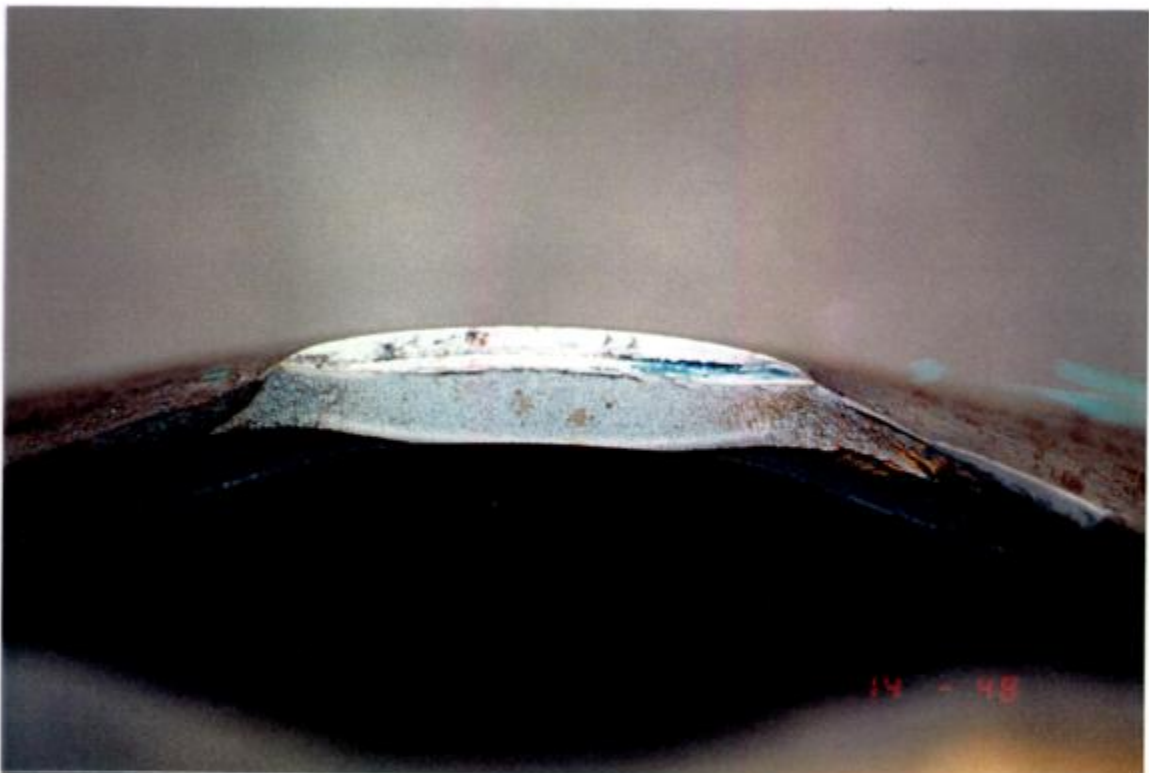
Zona del defecto en la probeta 2 (entalla y zona de ruptura)
